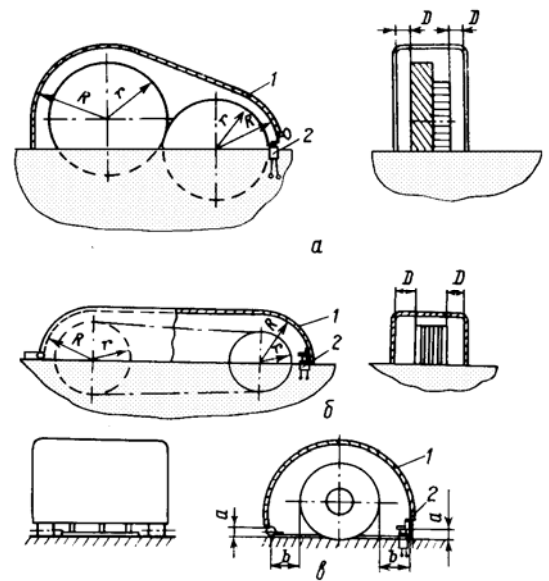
Огородження виступаючих передач, механізмів: а – зубчаті передачі; б – клиноремінні передачі; в – ножі, барабани (1 – відкидний кожух; 2 – блокування)
